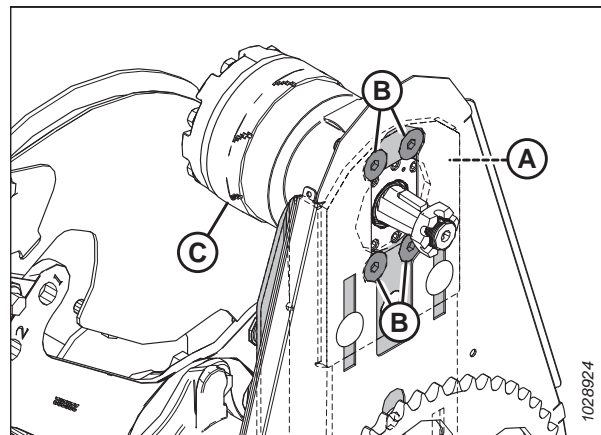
Tornillos de montaje del motor del mando del molinete
